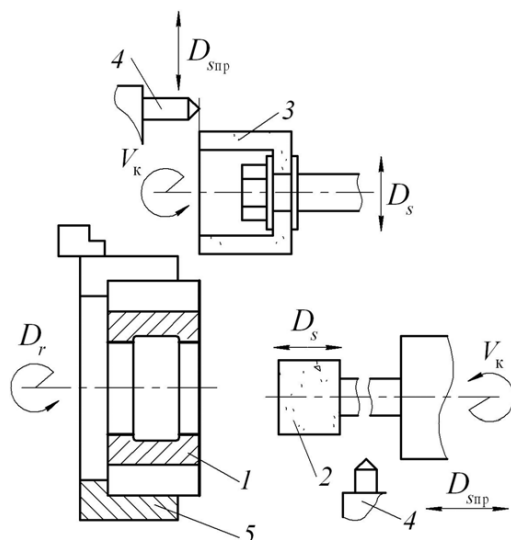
Шлифование базовых поверхностей инструмента насадного класса на внутришлифовальном станке: 1 – заготовка; 2 – шлифовальный круг для обработки отверстия; 3 – шлифовальный круг для обработки торца; 4 – правящие инструменты; 5 – разжимная втулка
